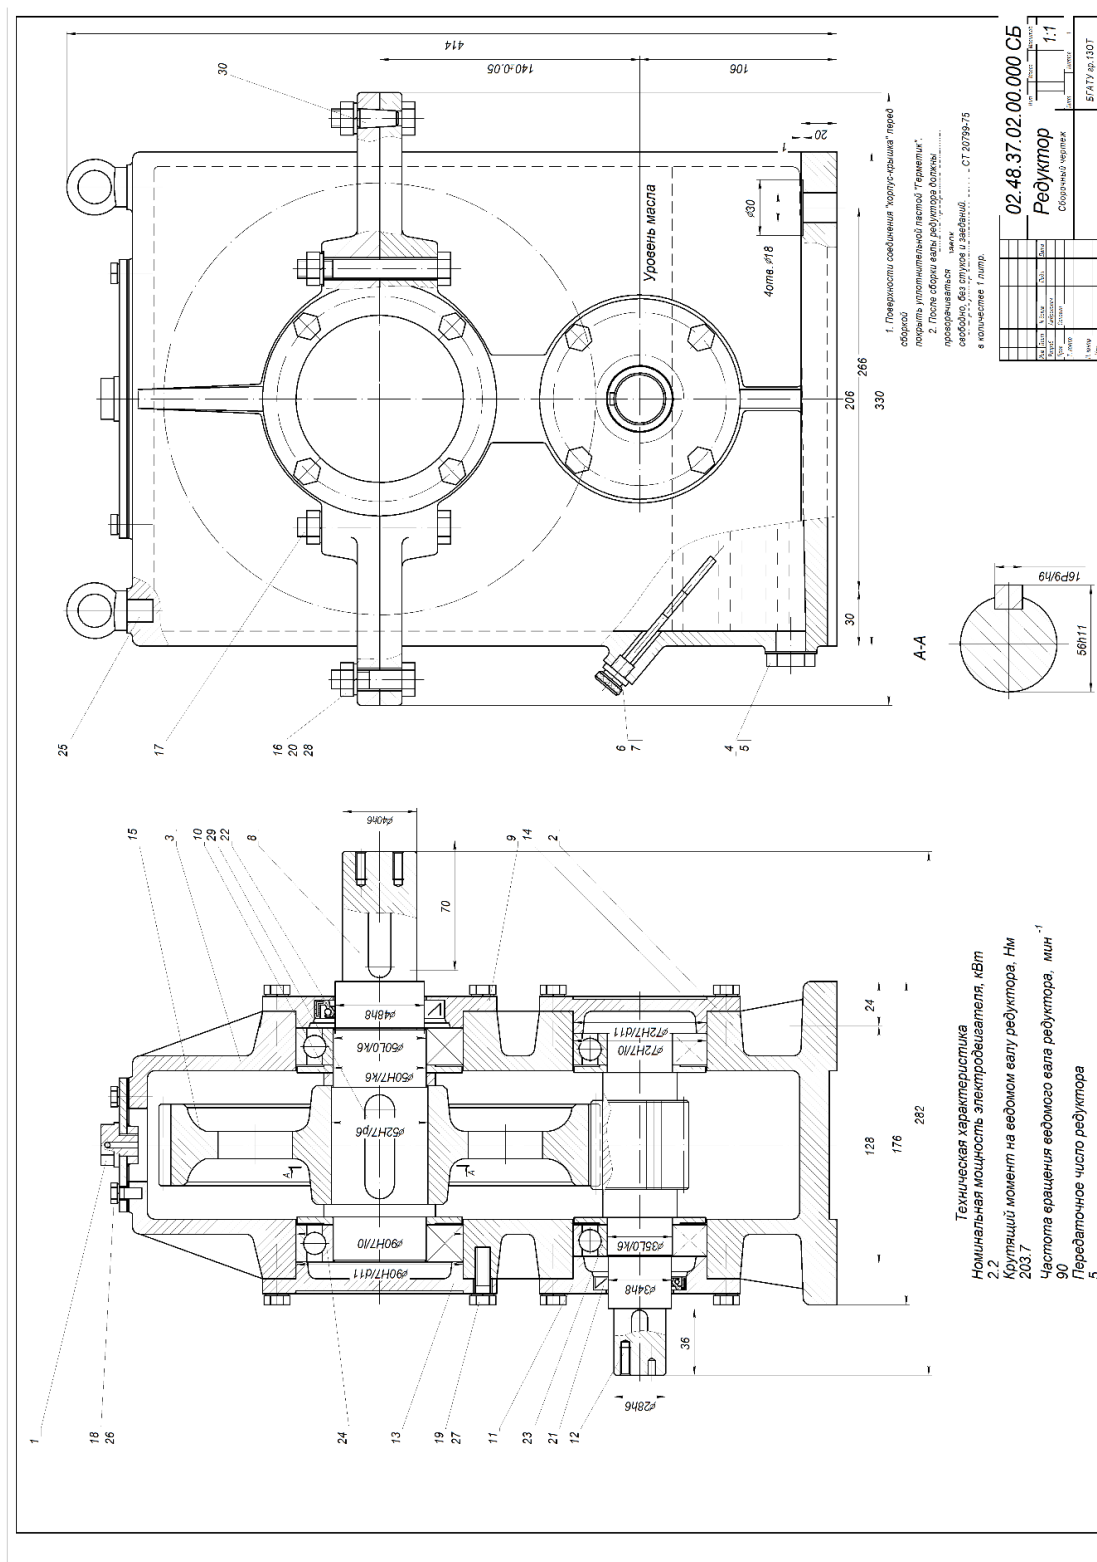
Редуктор цилиндрический одноступенчатый горизонтальный с классическим корпусом
